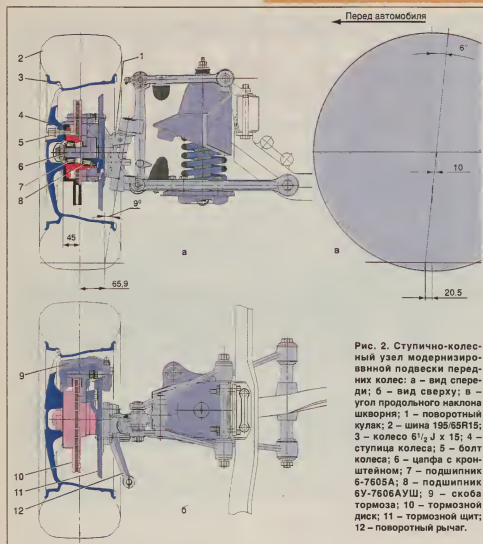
Ступично-колесный узел модернизированной подвески передних колес: а — вид спереди; б — вид сверху; в — угол продольного наклона шкворня; 1 — поворотный кулак; 2 — шина 195/65R15; 3 — колесо 6 $\frac{1}{2}$ J x 15; 4 — ступица колеса; 5 — болт колеса; 6 — цапфа с кронштейном; 7 — подшпильник 6-7605А; 8 — подшпильник 6У-7606АУШ; 9 — скоба тормоза; 10 — тормозной диск; 11 — тормозной щит; 12 — поворотный рычаг.
